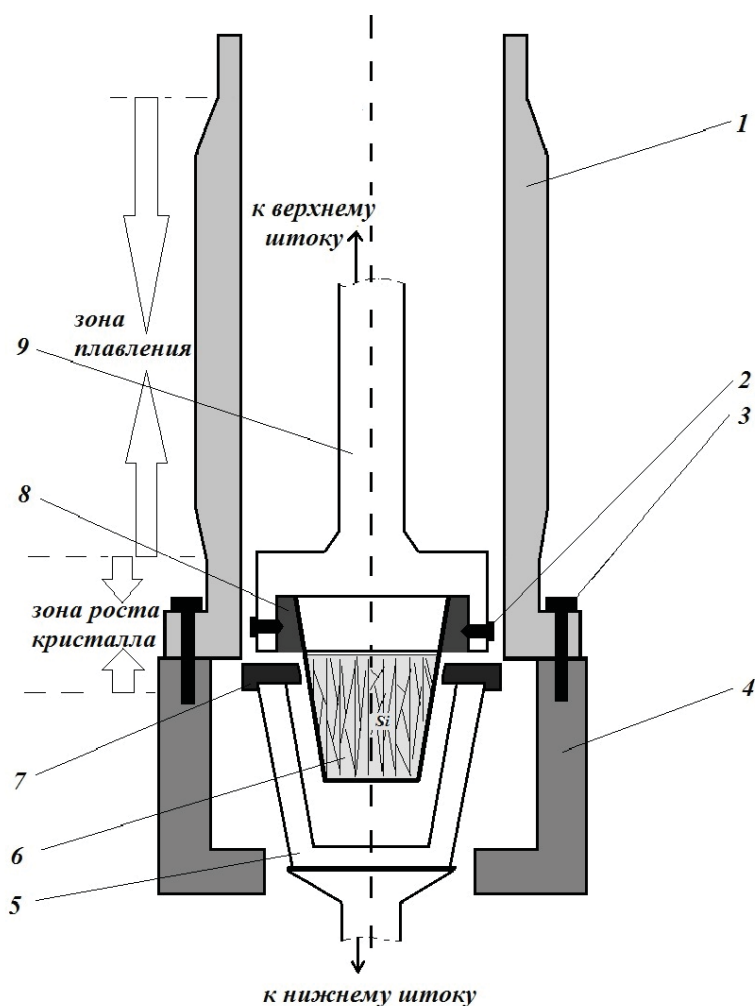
Схема крепления нагревателя и системы «тигель-расплав-кристалл» (материал — графит): 1- нагреватель; 2, 3- болты крепления тигля и нагревателя; 4- токоподводящие шины; 5- ловушка для тигля с кремнием; 6- слиток кремния в тигле из стеклоглерода; 7- диафрагма; 8- зажим тигля; 9- держатель тигля
